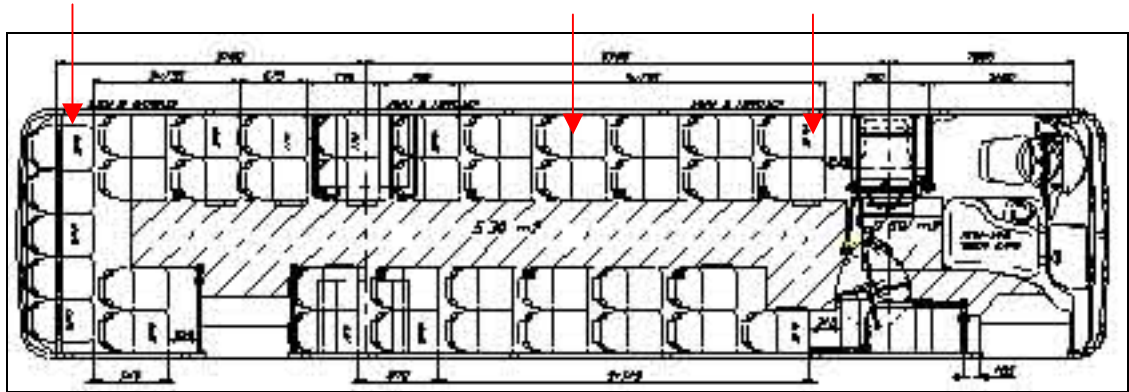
Lay-out visto de planta do ônibus carroceria Busscar
